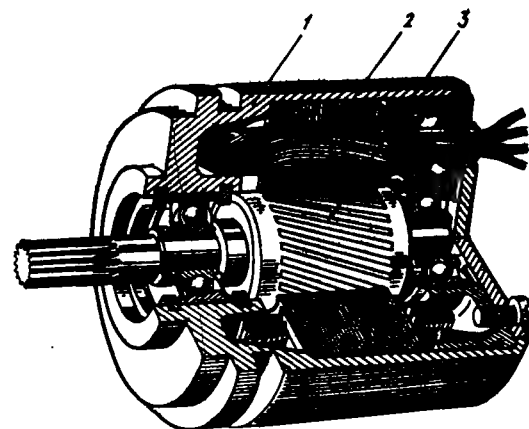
Асинхронный исполнительный двигатель ДКИ:
